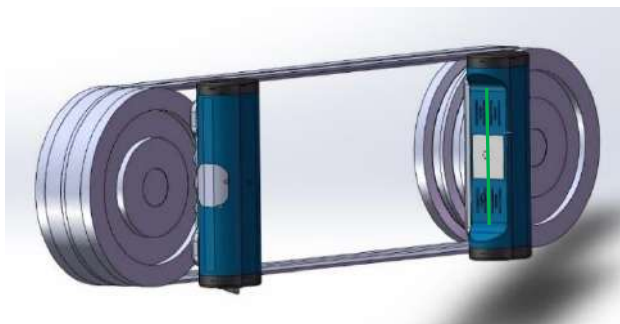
Блоки излучателя лазерного луча и отражателя установленные на шкивах
